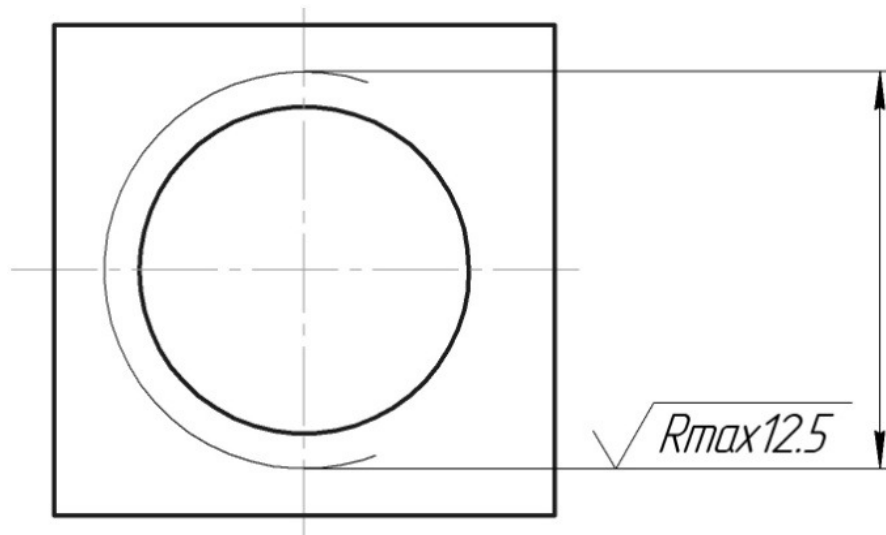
Пример обозначения шероховатости внутренней резьбы
